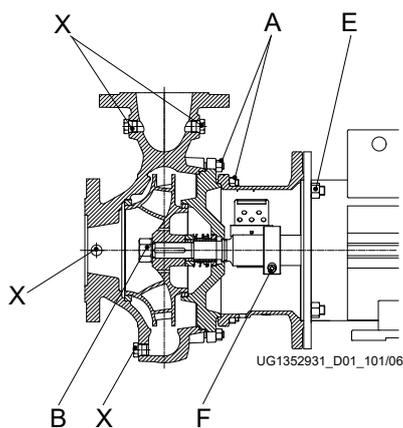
Punti di serraggio viti, versione con coperchio del corpo avvitato
